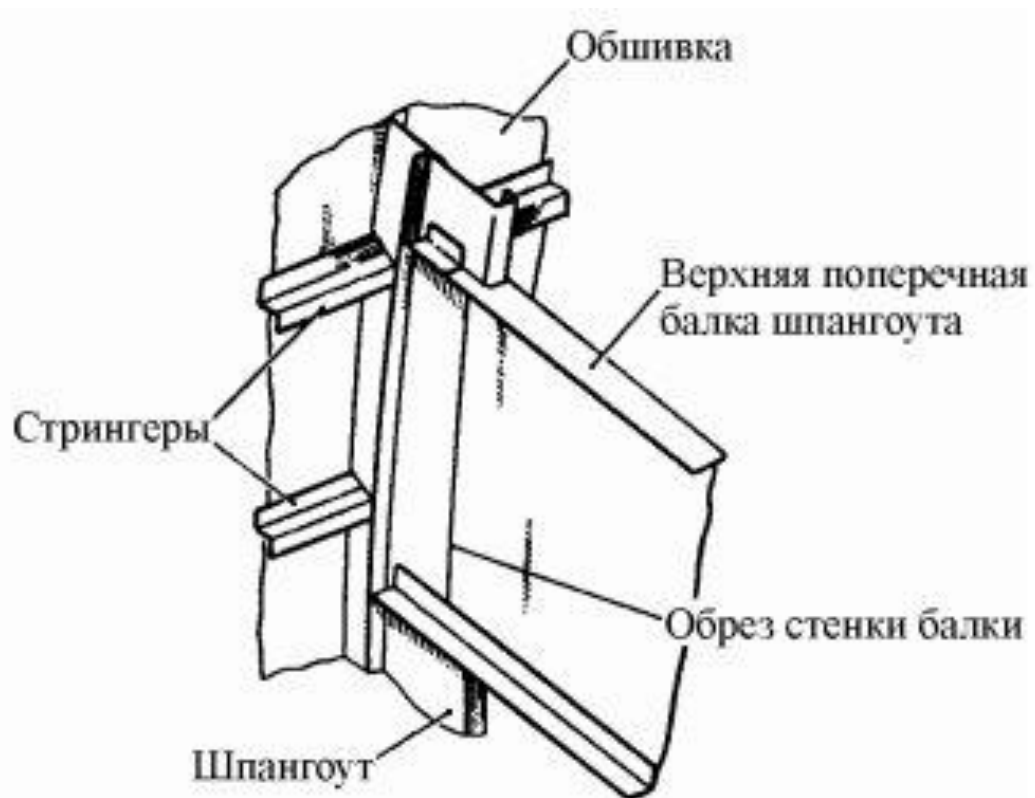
Крепление поперечной балки к ободу шпангоута
